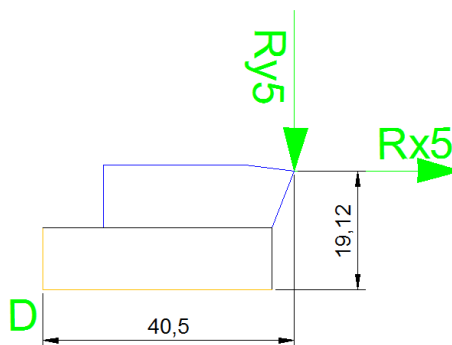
Fuerzas y distancias para la evaluación de la soldadura
